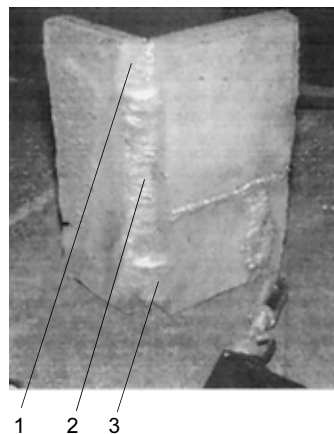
Фрагмент углового шва при сварке мощных шинопроводов полуавтоматом ПШ 107 ВА: 1—3 — сварные слои
